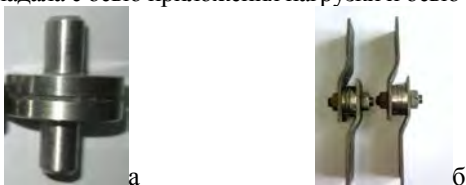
Образцы для испытаний на сдвиг (а -исходный, б –в приспособлении для испытания)
